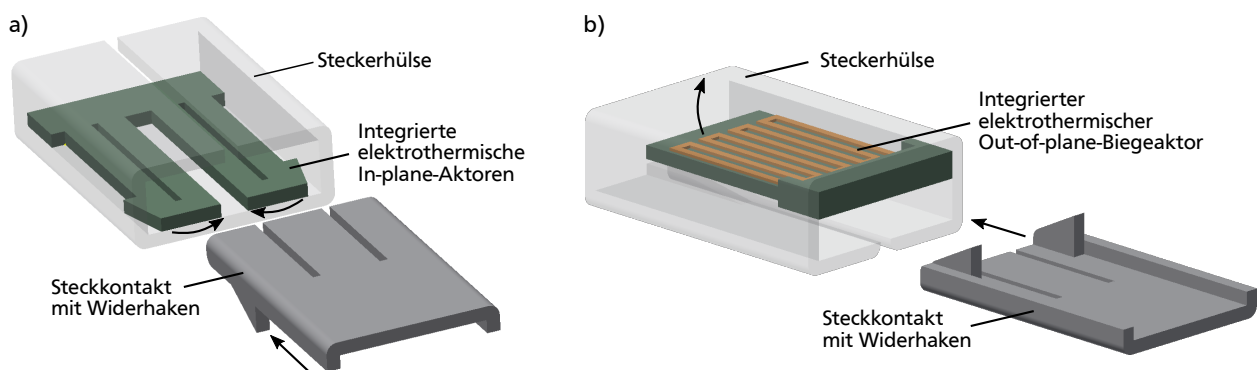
Demontageschutz mit elektrothermischen Aktoren für elektrische Steckverbinder gemäß der eigenen Patentschrift [503]: a) Ausführung mit In-plane-Aktoren; b) Ausführung mit einem Out-of-plane-Aktor.
